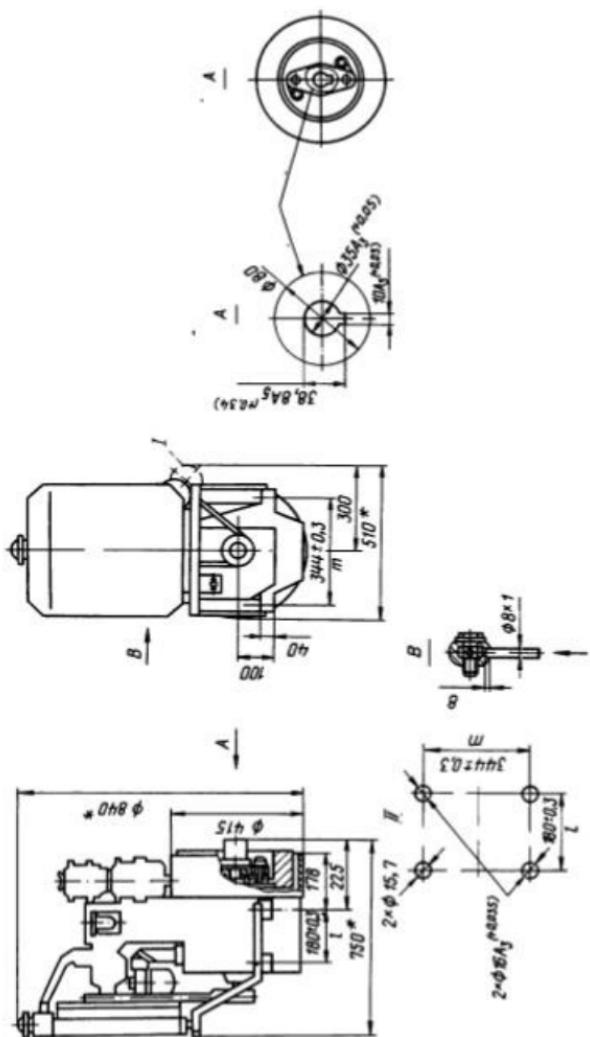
Габаритный чертеж дизеля 1Ч 8,5/11 (1П1-С):
